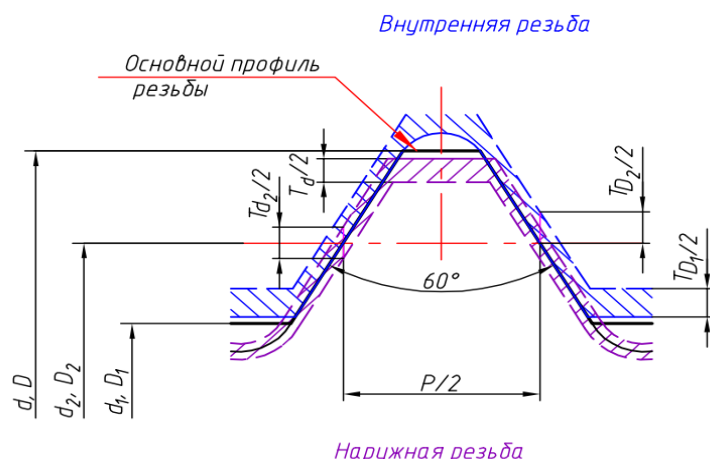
Расположение полей допусков в резьбовых переходных посадках
